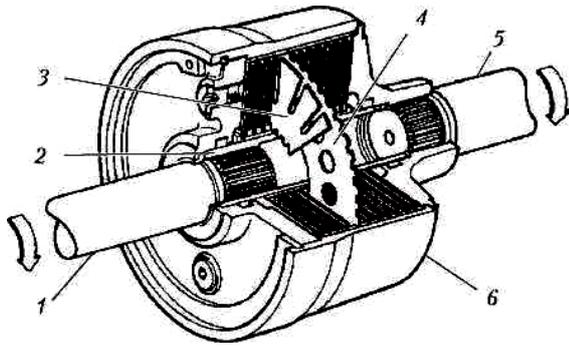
Вискомуфта: 1 — ведомый вал; 2 — втулка; 3 — диски, соединенные с ведомым валом; 4 — диски, соединенные с корпусом; 5 — ведущий вал; 6 — корпус
